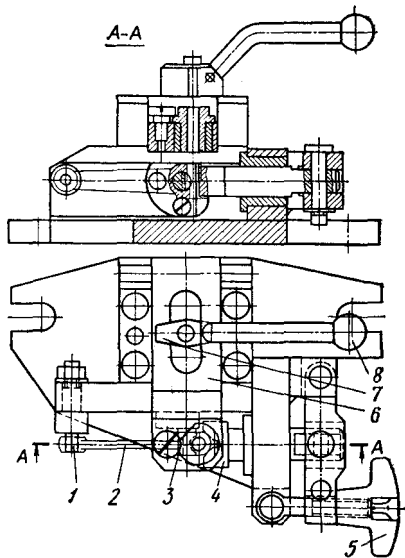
Приспособление для обработки отверстий в рычагах под зажим
